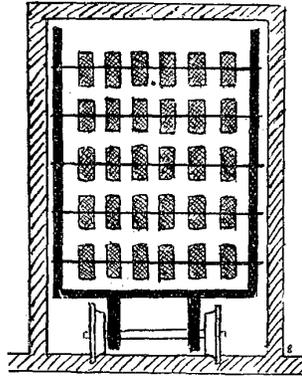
Coupe transversale d'un séchoir à tunnel.
